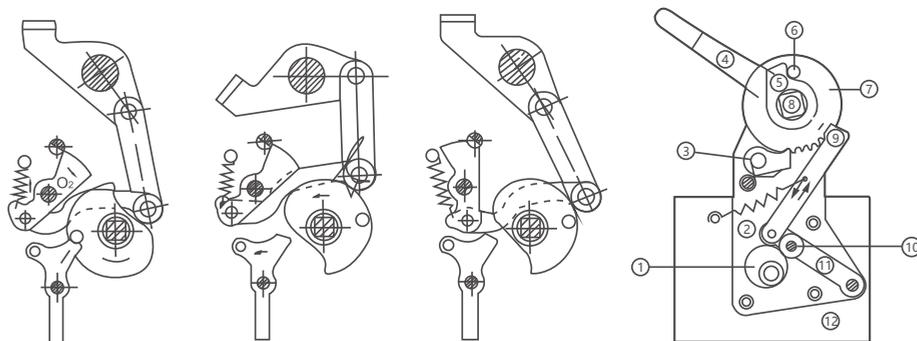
储能再扣位置 图9 闭合位置 图10 断开位置 图11 DW15-1600断路器电动及手动操作机构
